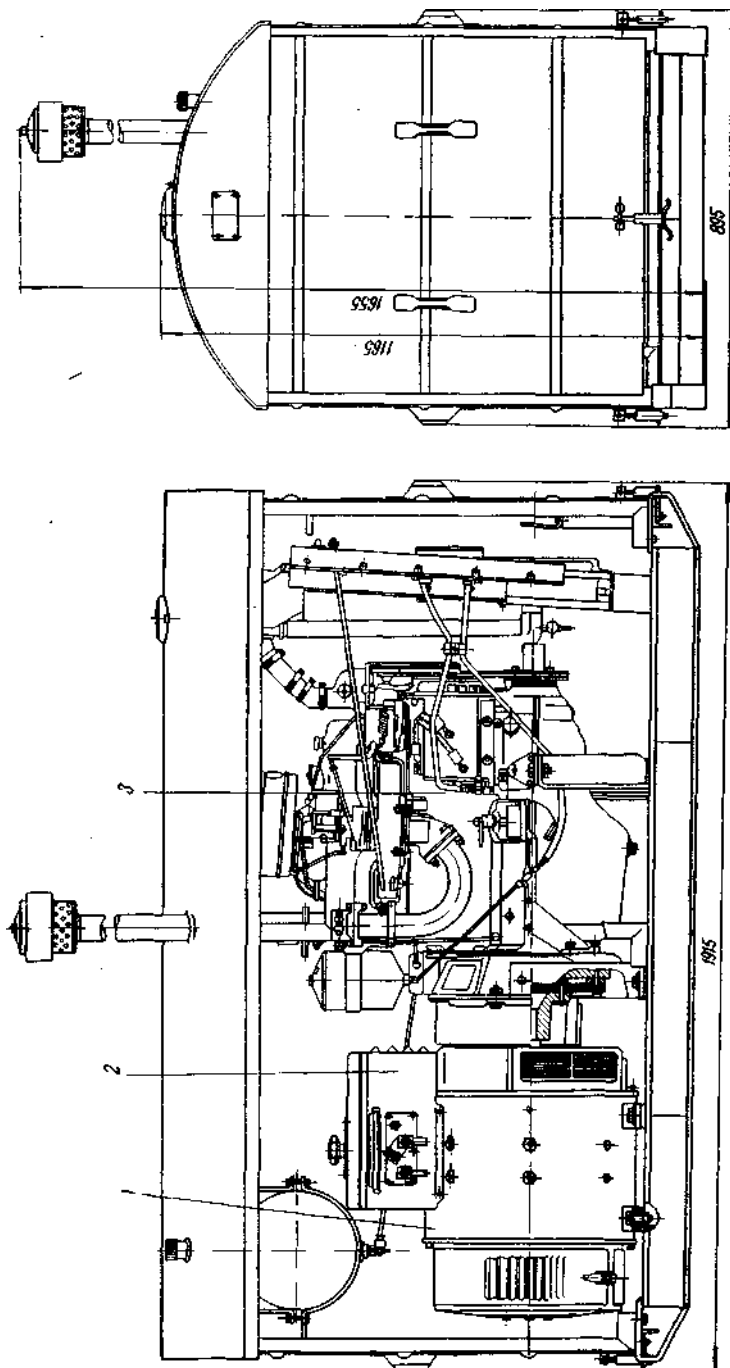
Однофазовой сварочный агрегат АСВ-300-VII.
